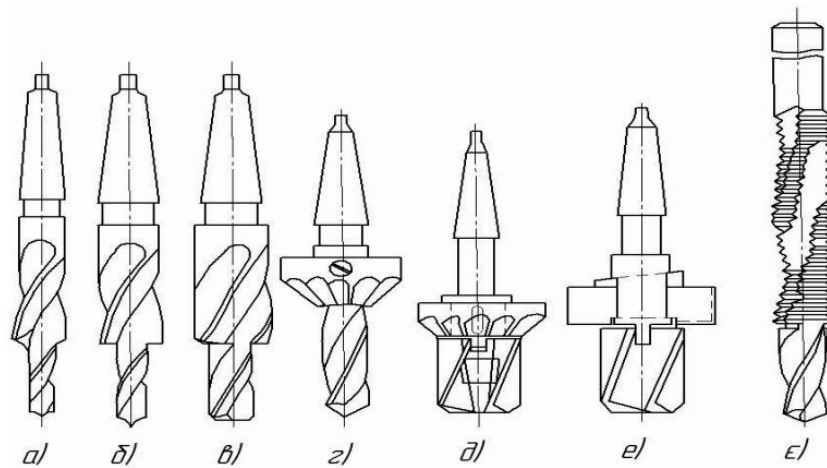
Комбіновані інструменти: а – ступінчасте свердло; б – свердло-зенкер; в – ступінчастий зенкер; г – свердло-зенківка; д – зенкер-зенківка; е – зенкер-цековка; є – свердло-мітчик
